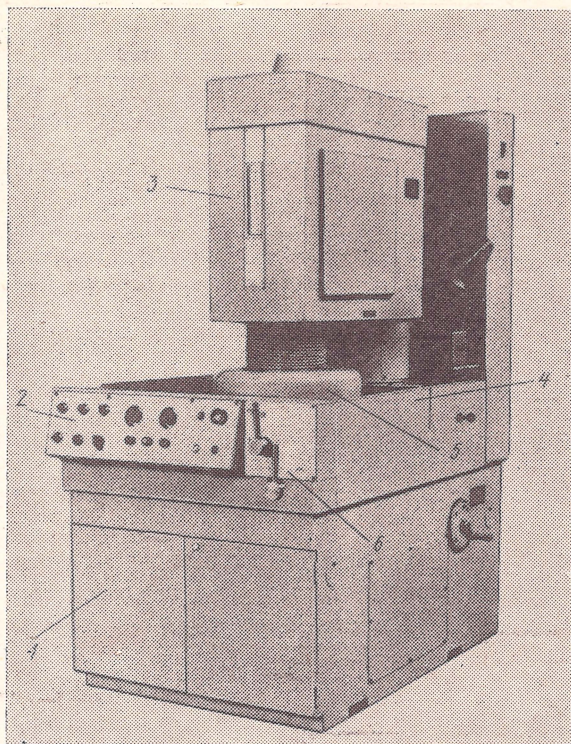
Универсальный вертикально-доводочный станок 3Д817
